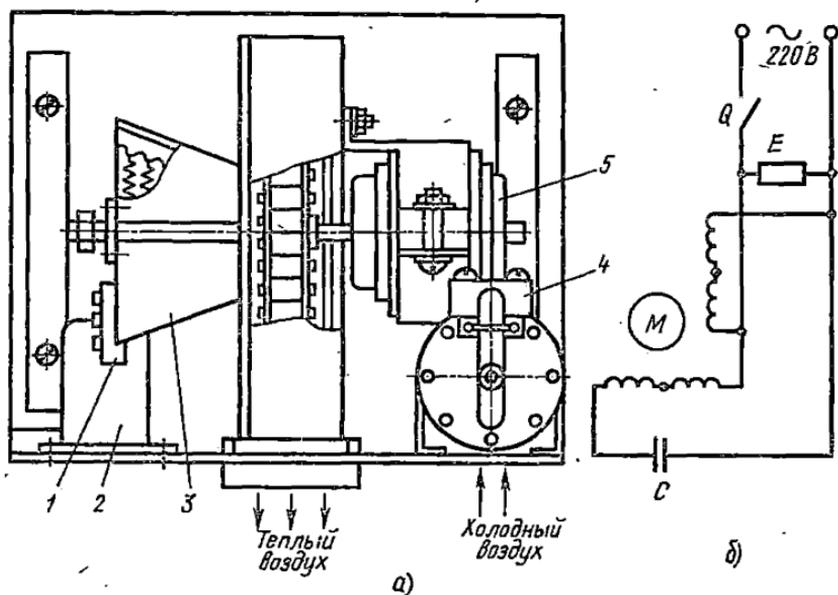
Общий вид (а) и схема (б) электрукоосушителя
